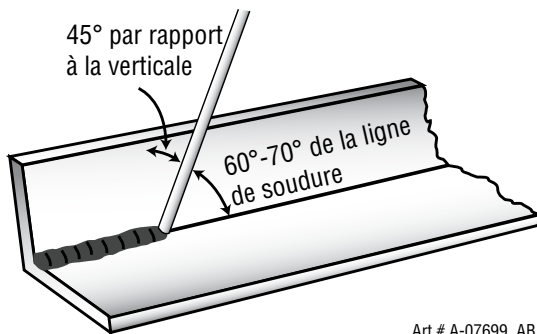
Position de l'électrode pour la soudure du joint HV
